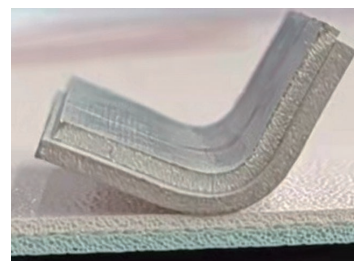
GH3230 高温合金薄板焊缝 90° 弯曲后试样
